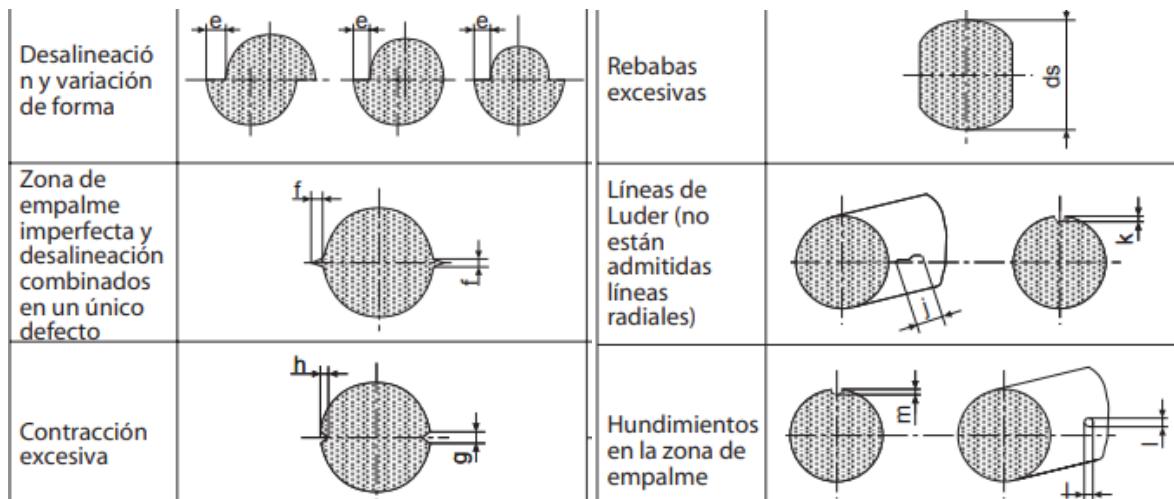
Toleràncies de forma i superfície segons la ISO 3601-3 [16]
